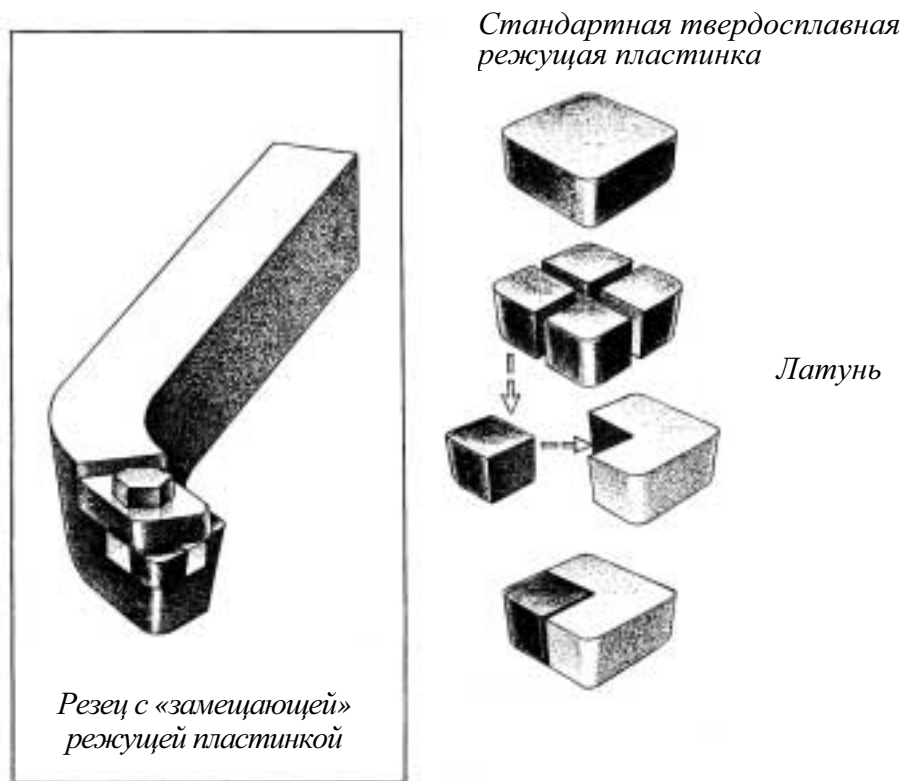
Схема с использованием режущих твердосплавных пластинок
